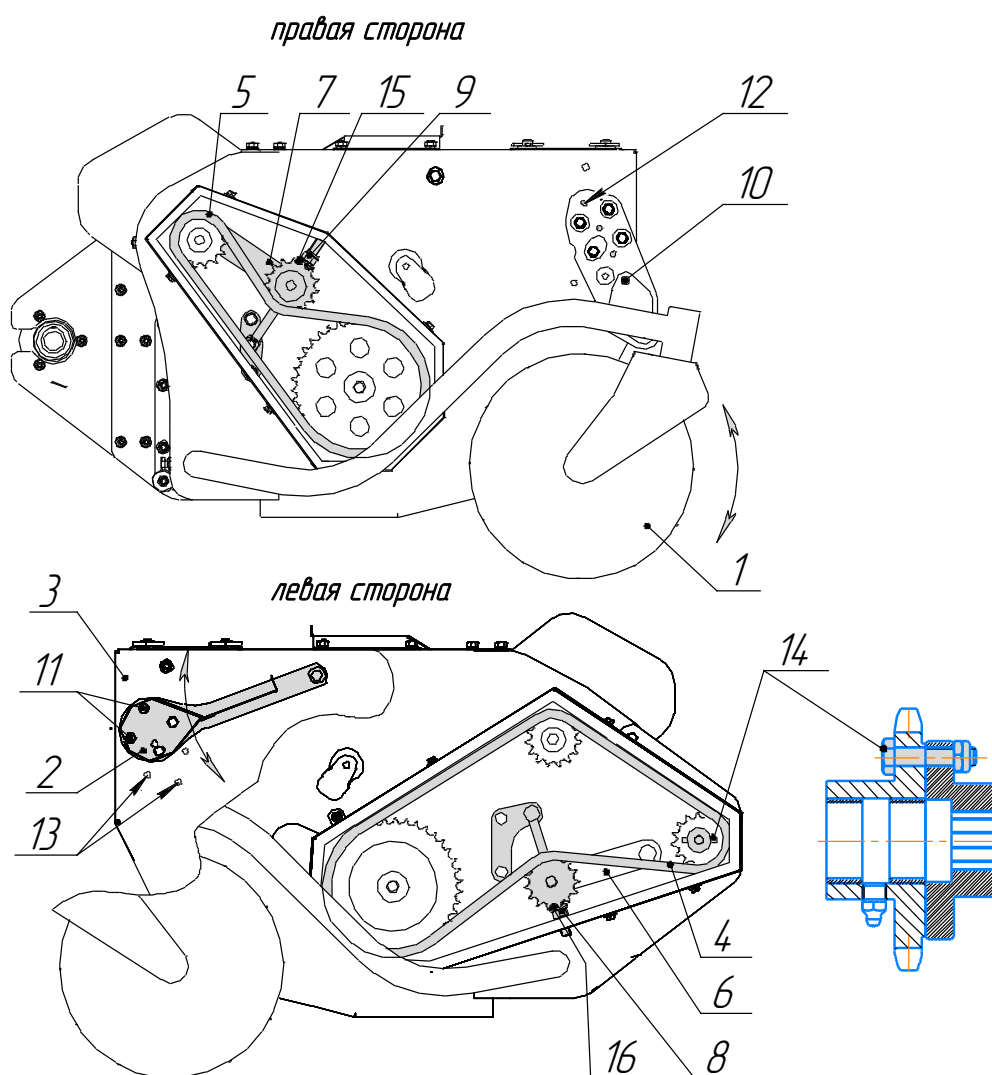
Регулировки подборщика: 1 – колесная опора; 2 – отражатель; 3 – корпус подборщика; 4 – цепь привода подборщика; 5 – цепь привода шнека; 6 – натяжитель цепи привода подборщика; 7 – натяжитель цепи шнека; 8 и 9 – регулировочные гайки; 10 – болт фиксации колеса; 11 – болты фиксации отражателя; 12 – регулировочные отверстия положения колес; 13 – регулировочные отверстия положения отражателя; 14 – предохранительный срезной болт; 15 и 16 – пружины.
